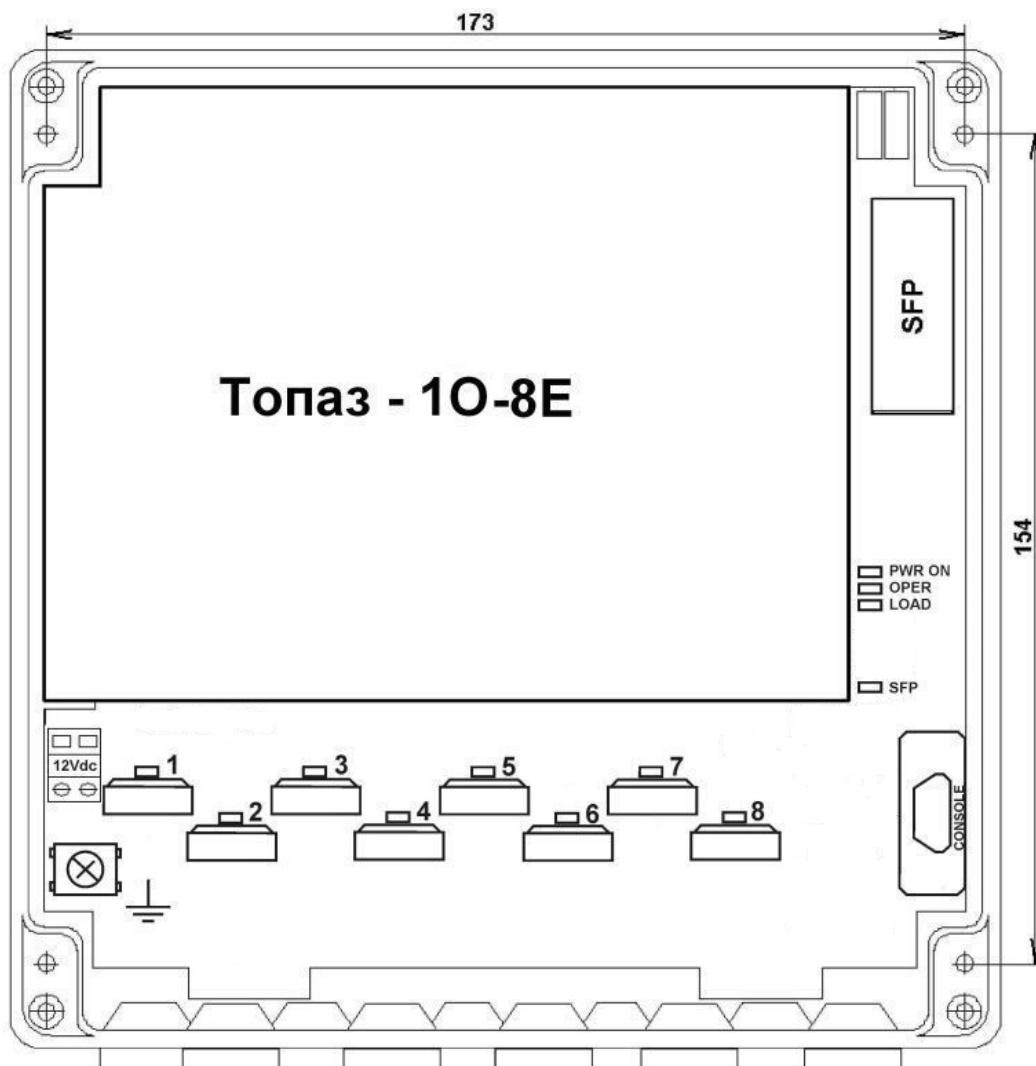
Внешний вид коммутатора Топаз-1о-8Е
